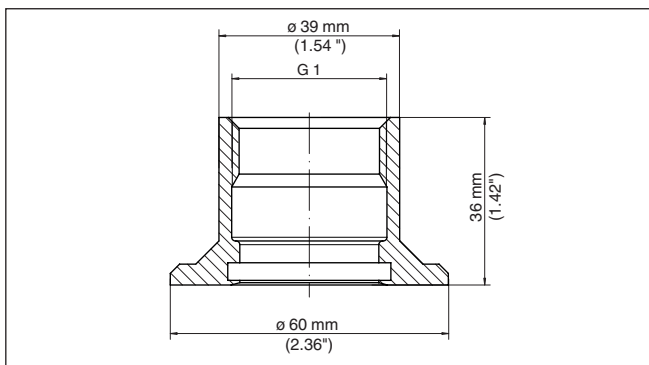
Dimensioni tronchetto a saldare G1 (DIN 3852-A)
